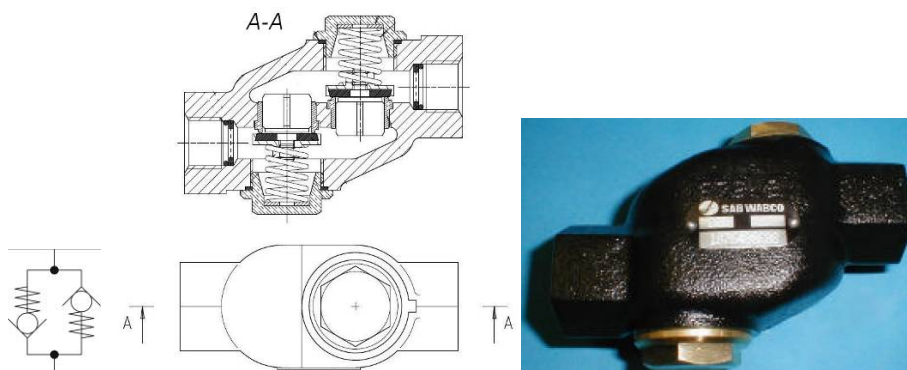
Zawór odcinający: 1 - wlot; 2 - wylot; 3 - atmosfera
